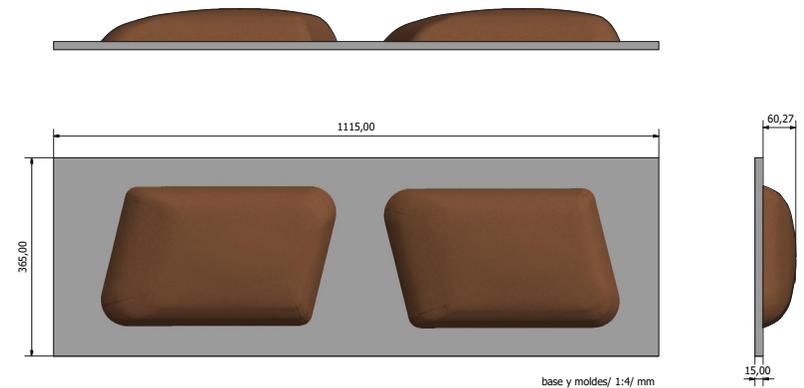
Dimensiones generales de moldes y marcos, para el moldeo del cuero. Elaborado por autor.
